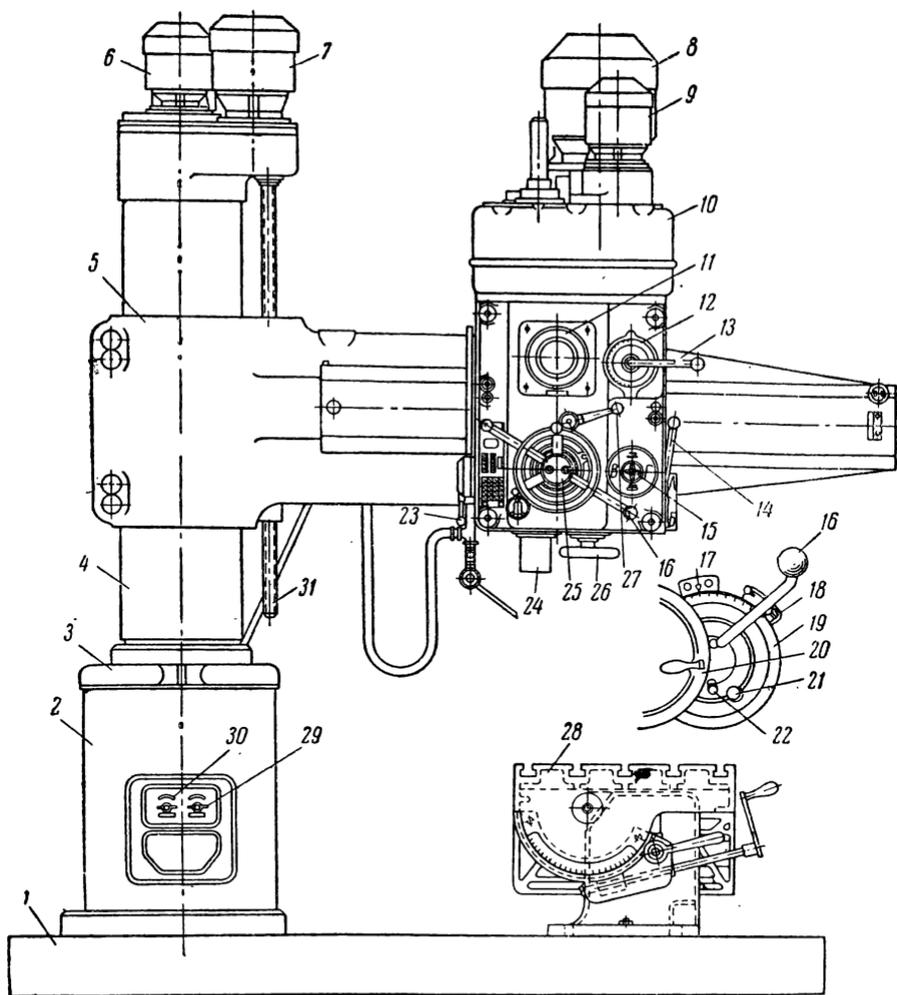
Общий вид радиально-сверлильного станка 2А55:
